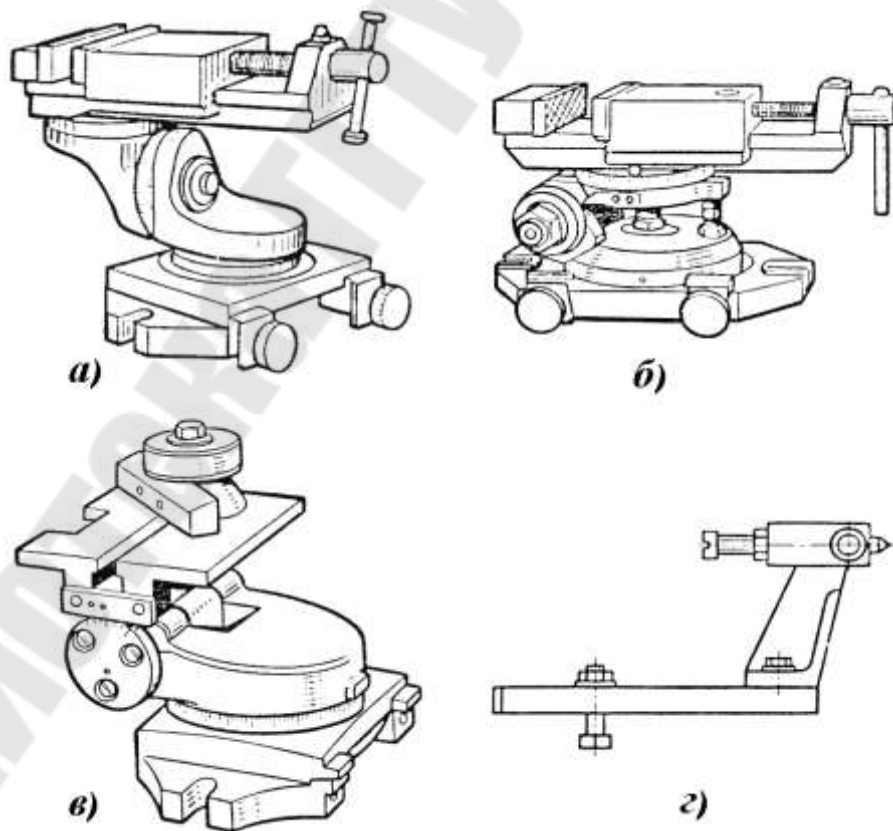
Эскизы универсальных тисков (*а*); наклонно-поворотных тисков (*б*); подручника (*в*); приспособления для линейной правки абразивного инструмента (*г*)
